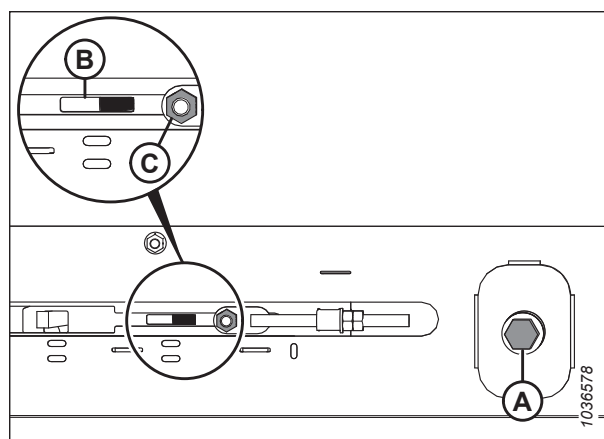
Ajuste del tensionador: se muestra el lado izquierdo; opuesto al lado derecho
